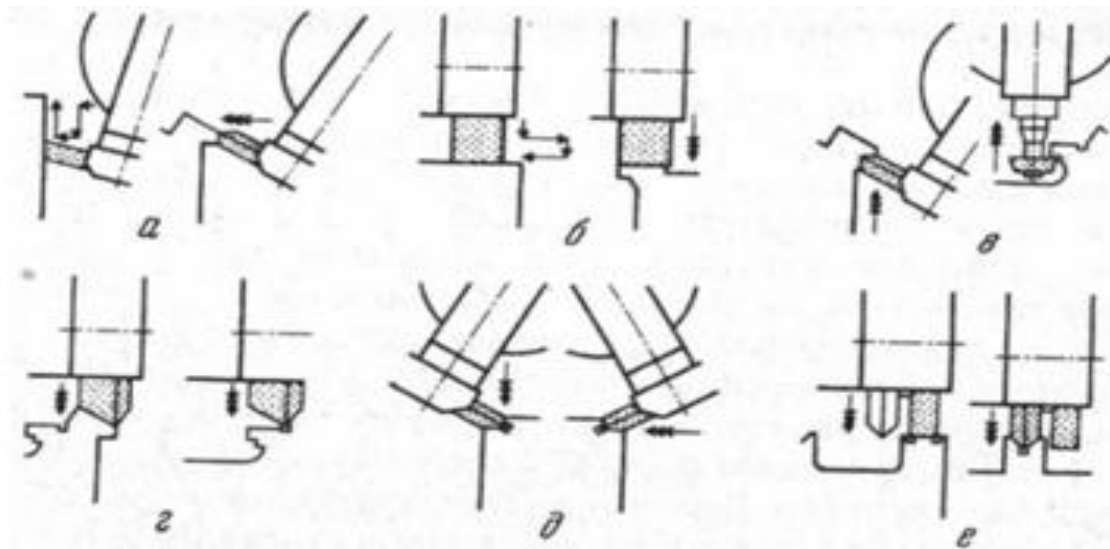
Типовые элементы направляющих и их обработка шлифованием: а – плоские поверхности направляющих с профильными шлифовальными кругами, б – плоские поверхности направляющих с кругами для периферийного шлифования, в – направляющая с нижним ползком, г – призматическая направляющая, д – направляющая в форме ласточкиного хвоста. е – призматические и плоские направляющие с набором шлифовальных кругов.
